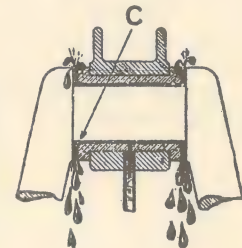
Os moentes gastos deixam passar óleo para o motor
